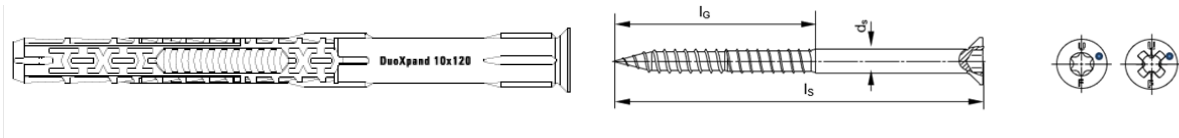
Technische Zeichnungen der Dübelhülse und Senkkopfschraube.
